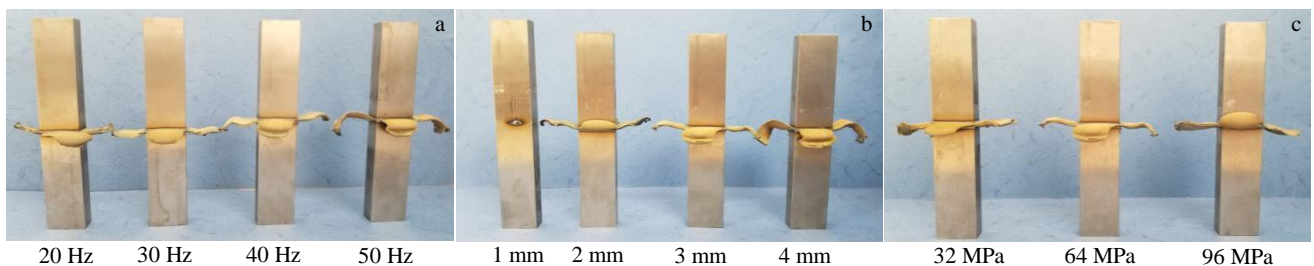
不同焊接工艺参数下 LFW 焊接接头形貌
